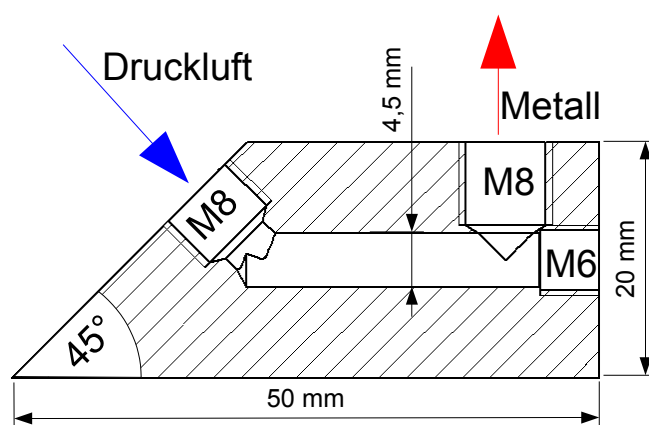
Schnittbild durch das Heizgefäß, in dem das Metall vor der Beschleunigung geschmolzen wird. Die Druckluft (blauer Pfeil) wird von links in den Hohlraum, der sich mittig befindet, gepresst. Der Hohlraum hat einen Durchmesser von 4,5 mm. Das Bohrloch lässt sich auf der rechten Seite mit einer „M6“-Schraube verschließen. Der Hohlraum wird komplett mit flüssigem Metall gefüllt, sodass die Pressluft das Metall durch die einzige Öffnung nach oben hinaus drückt (roter Pfeil). Um das Metall zu schmelzen, ist das Heizgefäß mit Heizdraht umwickelt. „M8“ und „M6“ stehen für die Gewindtypen.
